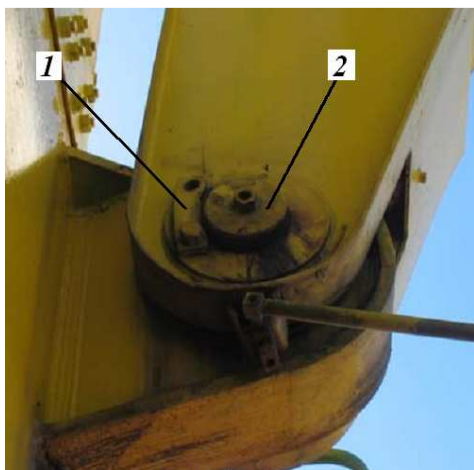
Корінний шарнір стріли в аварійному стані: 1 – ригельна планка; 2 – палець
